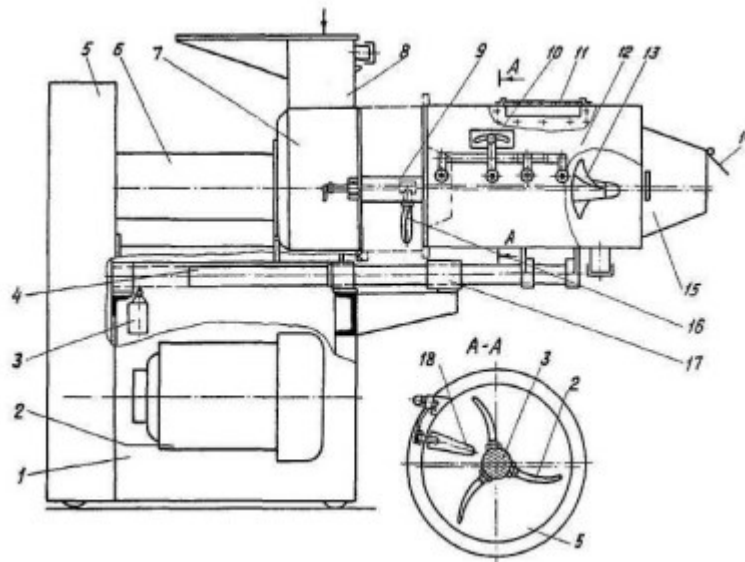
Високоінтенсивна тістомісильна машина ЦАИГ-ХТК: 1 - станина; 2 - електродвигун; 3 - кінцевий вимикач; 4 - напрямна; 5 - огорожа; 6 - корпус з підшипниками; 7 - стаціонарна частина робочої камери; 8 - борошняний патрубков; 9 - місильний вал; 10 - регулятор; 11 - вікно для догляду; 12 - змінна частина робочої камери; 13 - пластифікатор; 14 - регулюючий пристрій; 15 - вихідний корпус; 16 - робоча лопать; 17 - напрямні; 18 - гальмівна лопать
